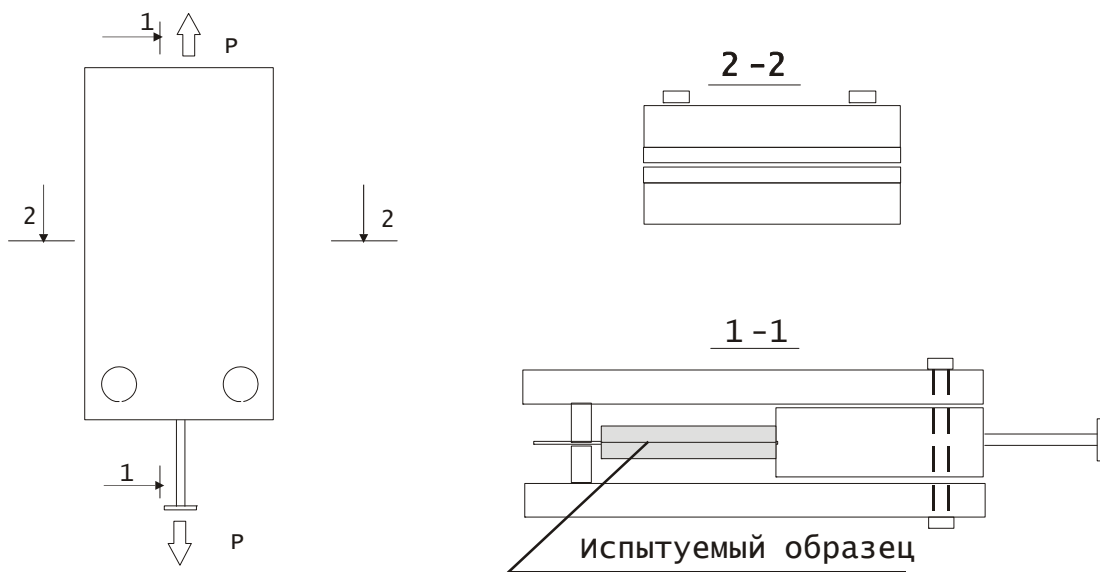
Приспособление для испытания образцов с огнезащитным покрытием
